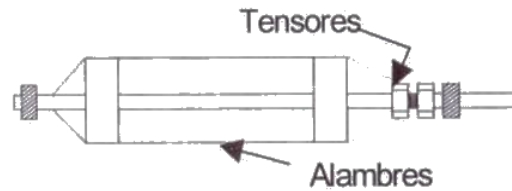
Vista frontal de mecanismo de corte por alambre.
